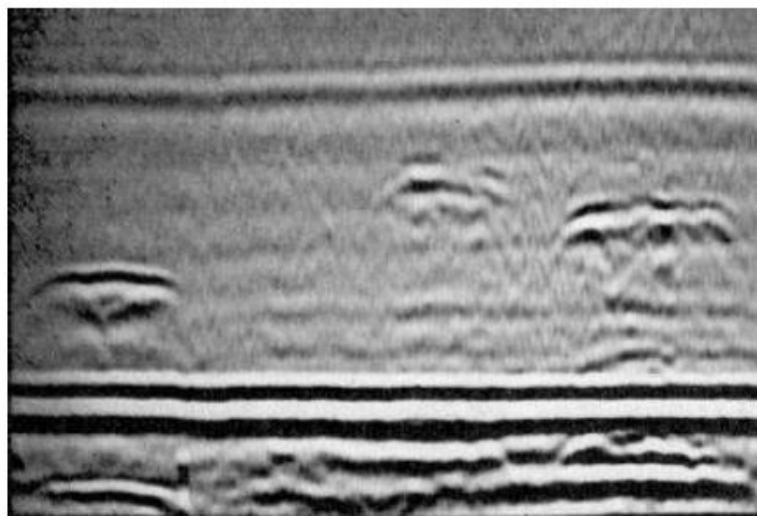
Barrido TOFD, scan-B para junta soldada en T
